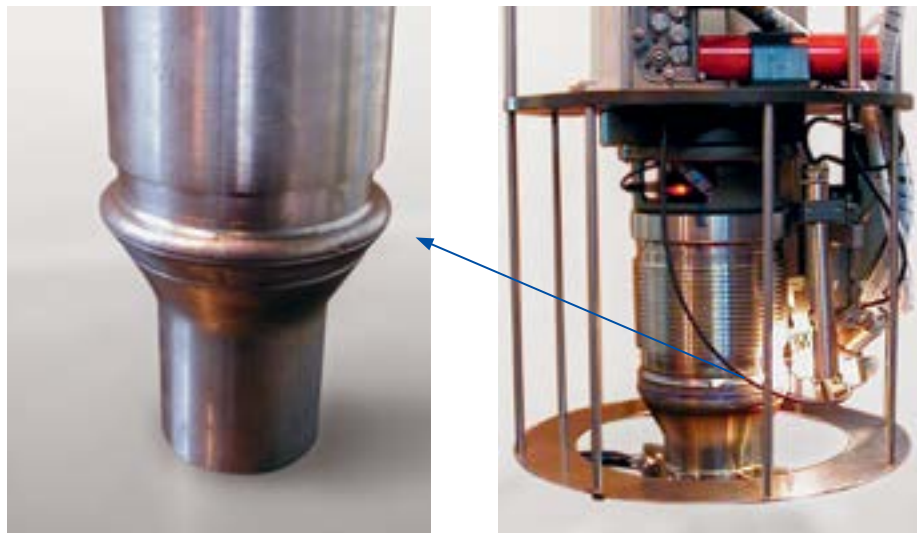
Восстановление внешней поверхности переходника крышки ядерного реактора
